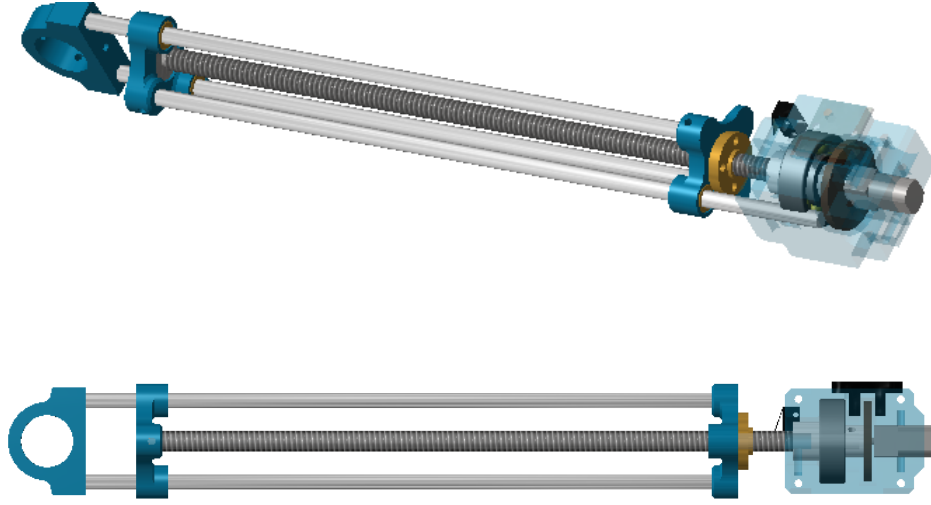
Articulación prismática, ver sección de Anexos para un plano detallado de la estructura
